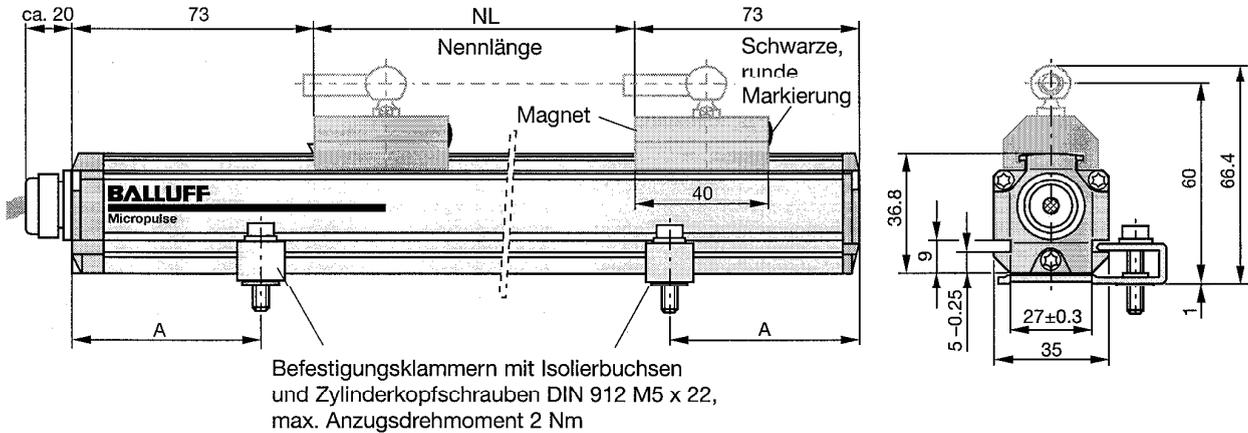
Maßzeichnung (Wegaufnehmer BTL5...P-KA.. mit geführtem Positionsgeber BTL5-F-2814-1S)
